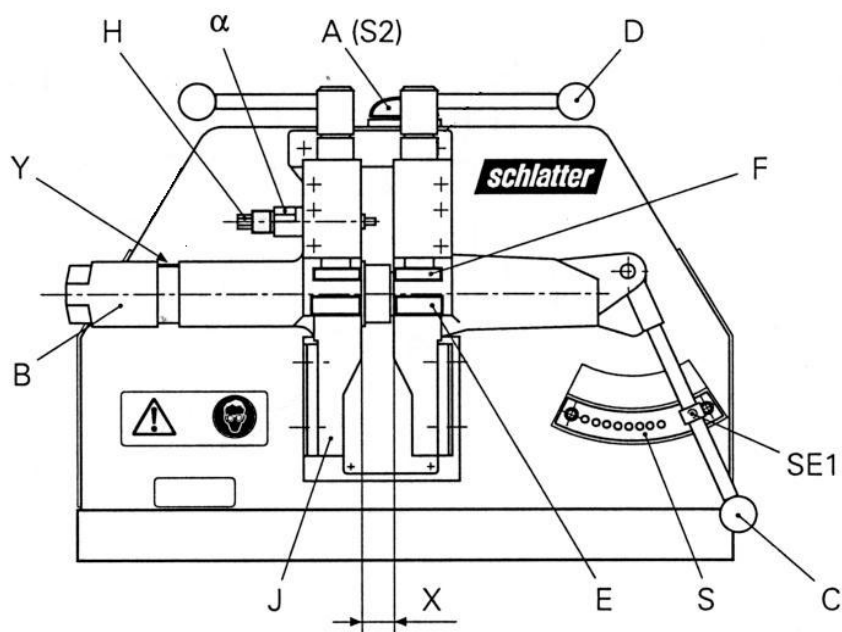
Máquina de soldar a topo tipo M , tabela de ajuste
